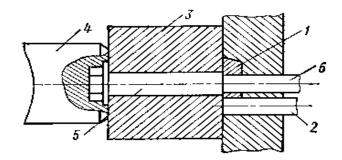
Схема штампового инструмента однопозиционного горячештамповочного автомата A315A для высадки болтов: 1 — нож; 2 — пруток; 3 — матрица; 4 — пуансон; 5 — поковка; 6 — выталкиватель
